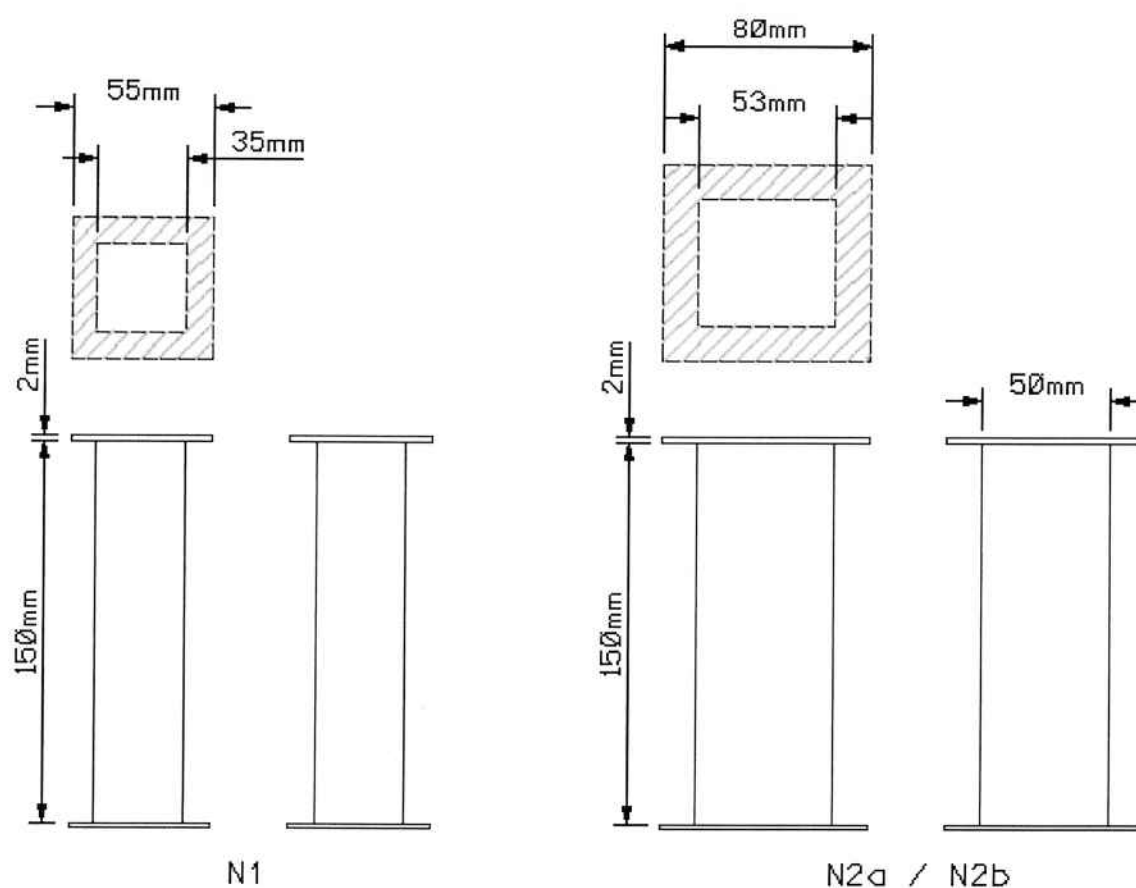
Vistas e dimensões dos moldes para as bobinas AC
